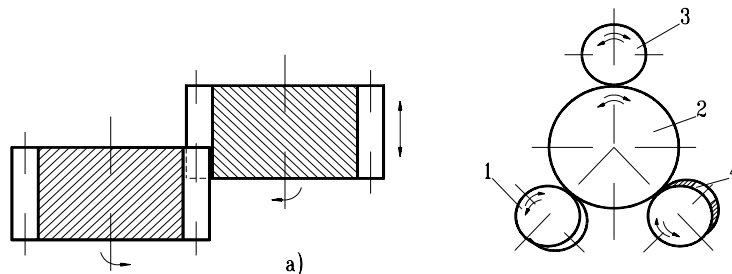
Схемы притирки зубьев зубчатых колёс:
